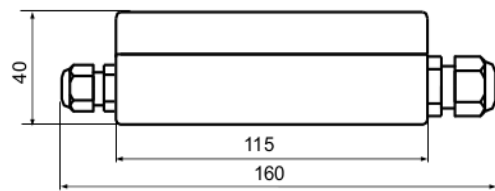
Габаритные и установочные размеры блока модулей БМ-4
